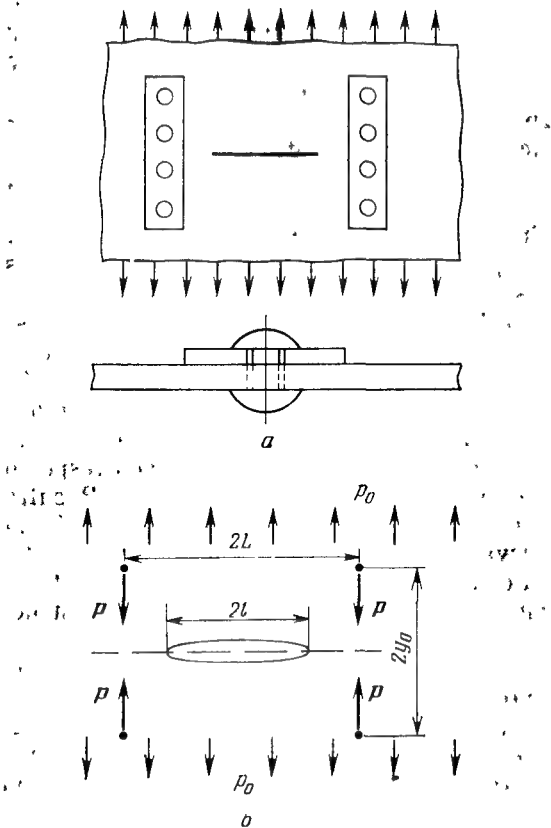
Panel con remachadas nervaduras de refuerzo (a) y esquematización del problema sobre la grieta en una hoja con nervaduras de refuerzo.
